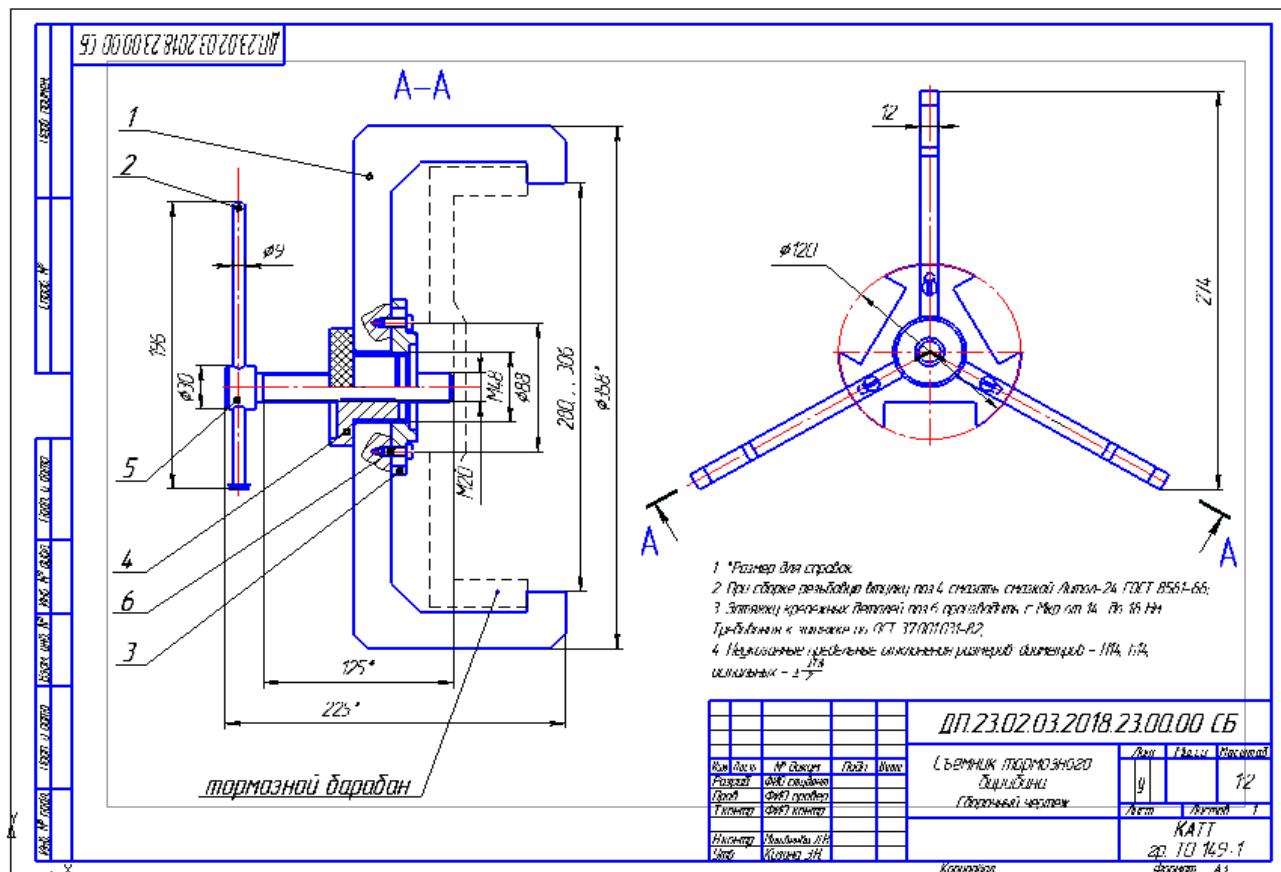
Пример оформления сборочного чертежа – СБ
